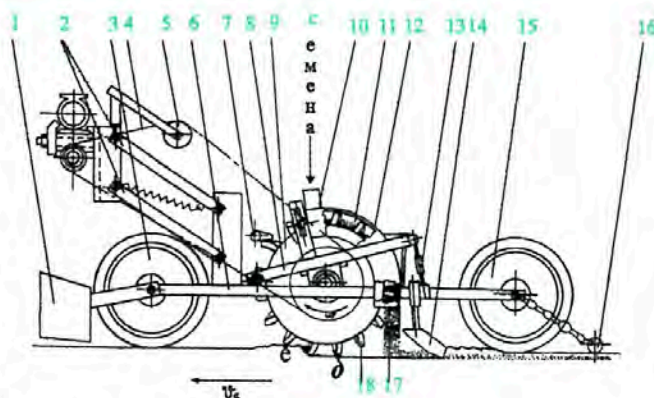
Конструктивная схема сошника: 1 — стойка со щеками; 2 — параллелограммная подвеска; 3 — передний пневматический уплотняющий каток; 4 — цепной привод; 5 — поддерживающий ролик; 6 — несущая рама; 7 — чистик; 8 — рама; 9 — цилиндрический бороздообразующий барабан; 10 — семянаправитель; 11 — семяпроводы; 12 — П-образный кожух; 13 — винт-регулятор глубины заделки семян; 14 — загортач; 15 — задний пневматический уплотняющий каток; 16 — шлейф; 17 — семяраспределитель; 18 — эластичные лопасти прямоугольной формы.
